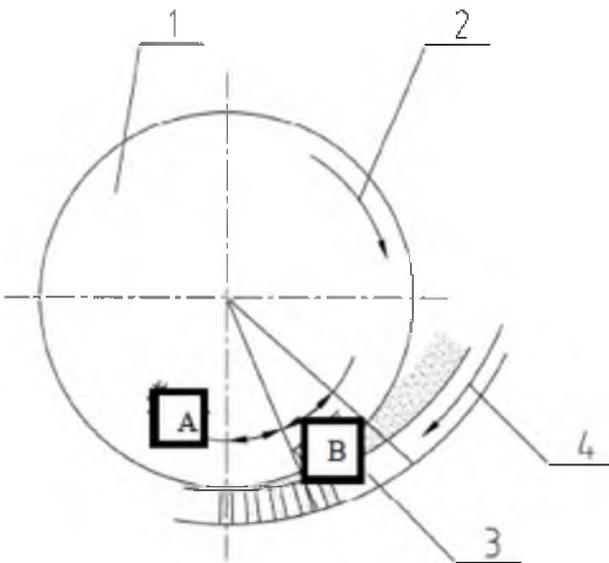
Fuerzas de compresión entre el rodillo y el dado
